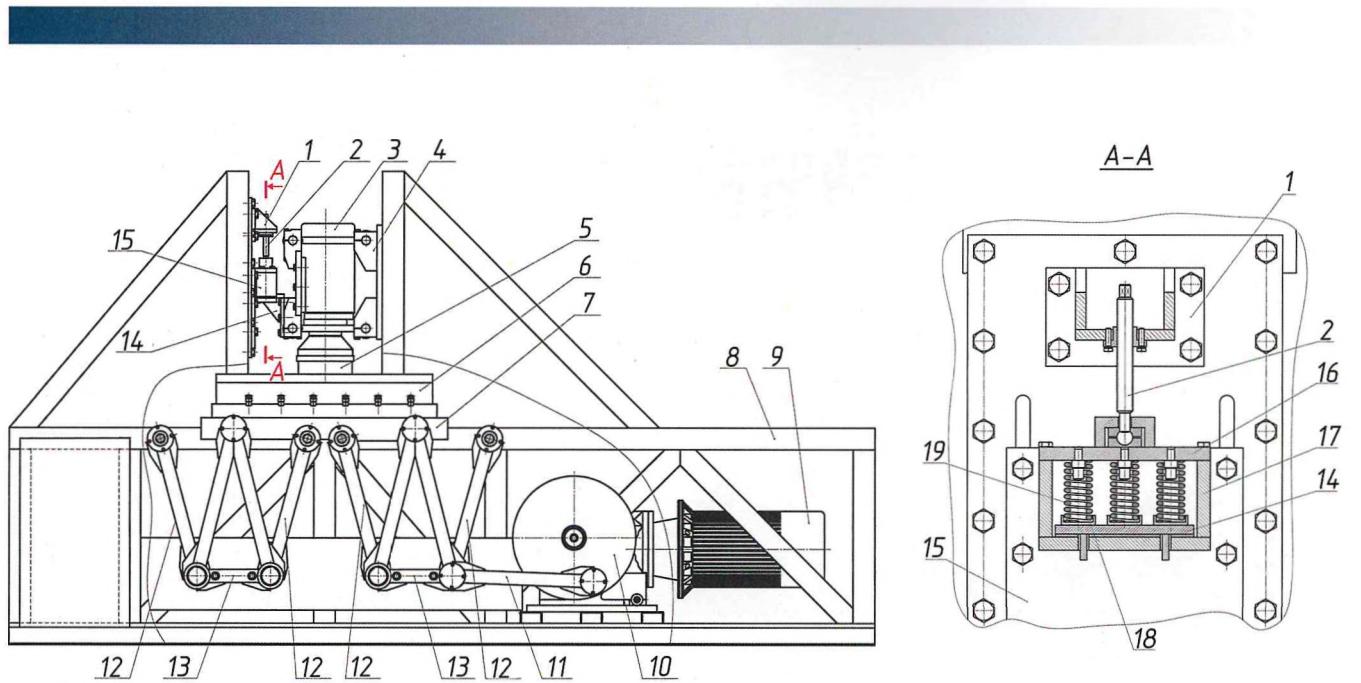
Стенд для испытания рельсошлифовальных кругов;
